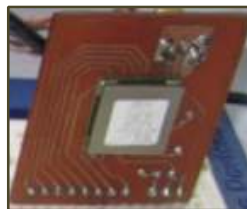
Montaje y soldadura del módulo GPS y conector sma sobre Placa PCB
